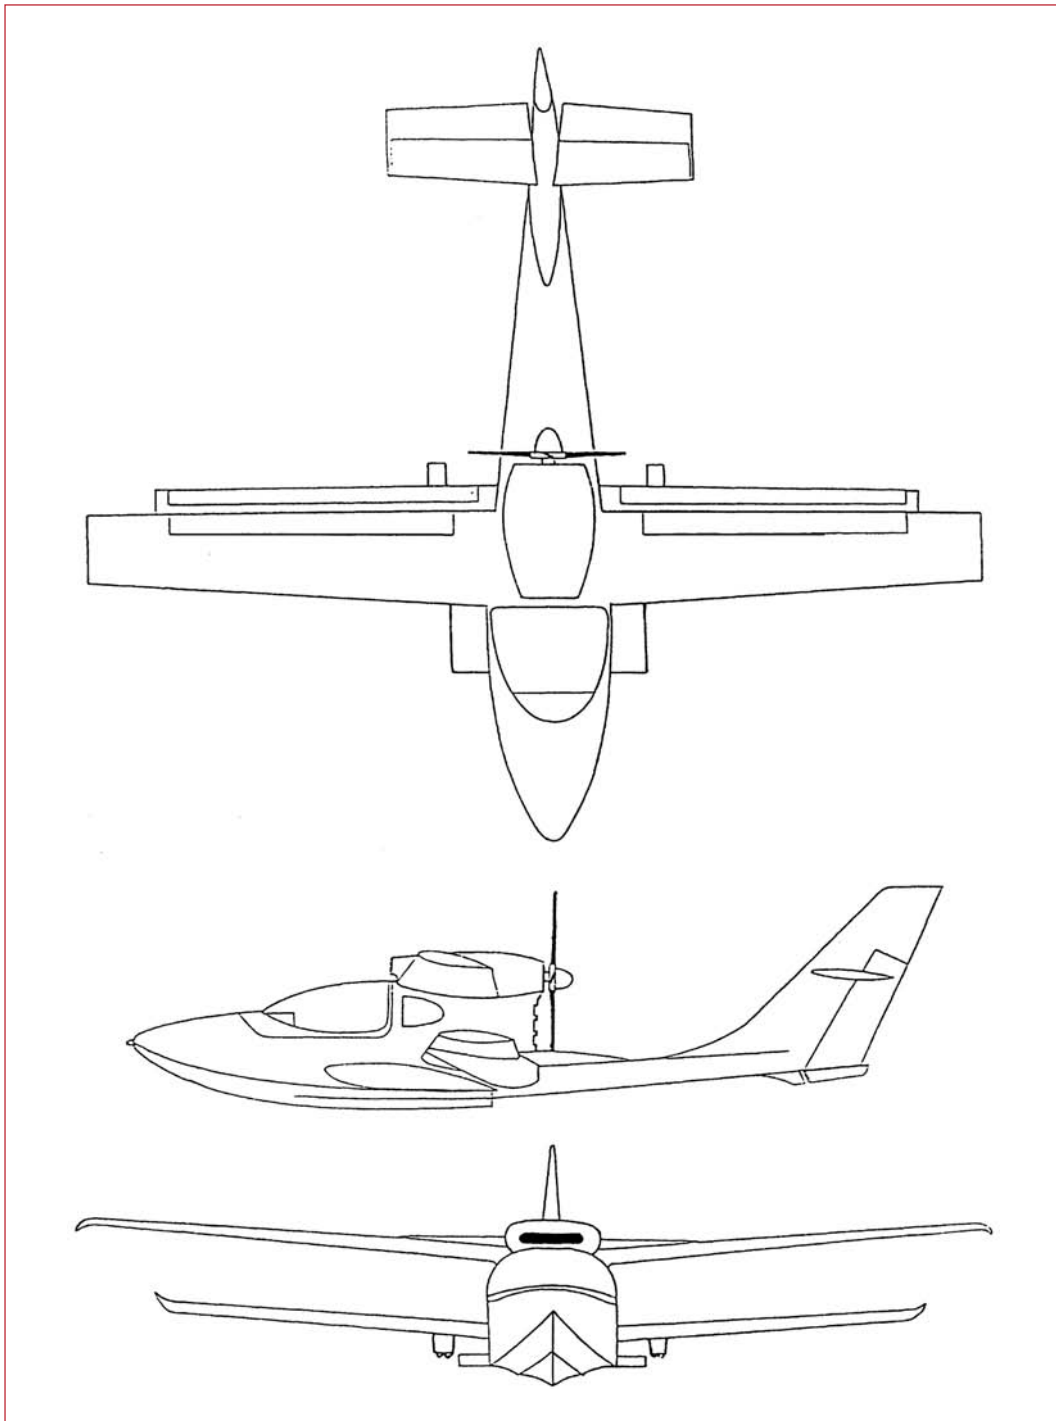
Plano tres vistas del avión con el tren retraído
